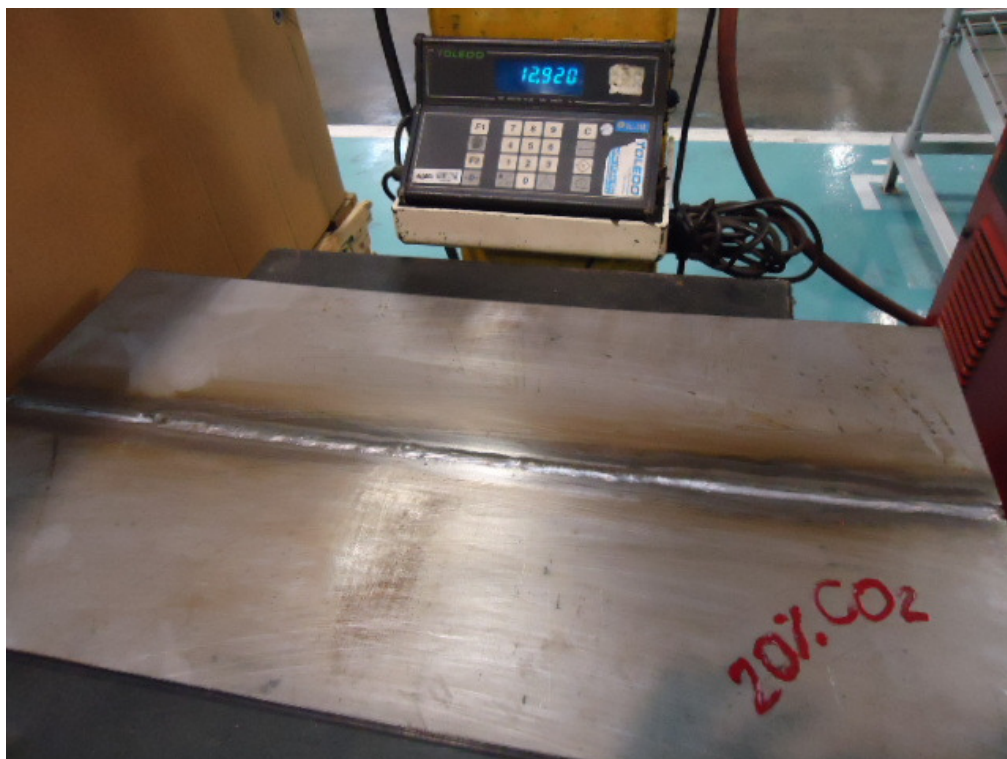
Chapa após a soldagem com mistura 20% CO₂
